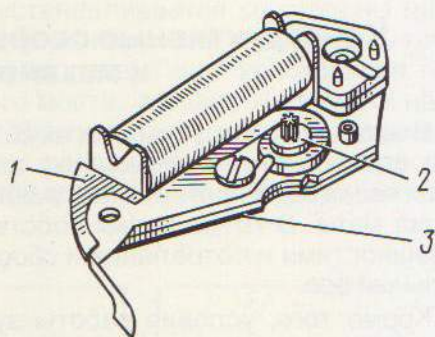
Шаговый двигатель с вынесенной катушкой:
